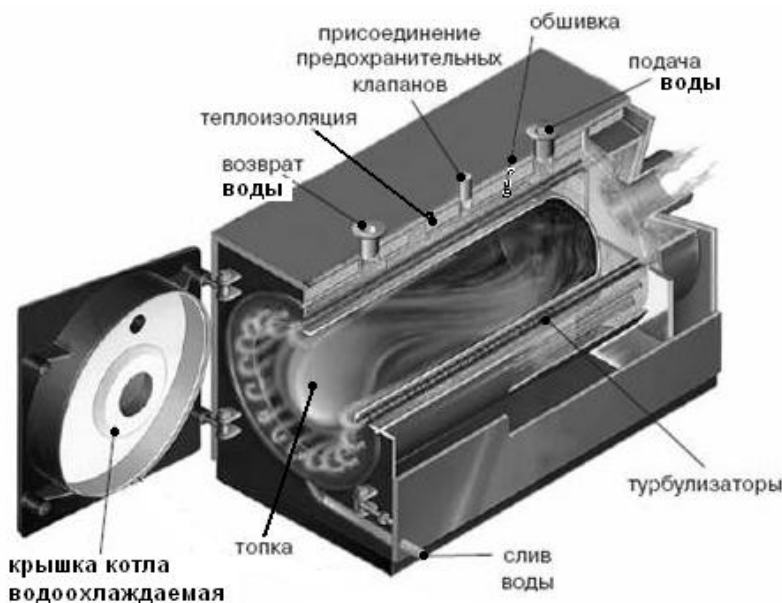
Схематический разрез двухходового жаротрубного котла с реверсивной топкой.
